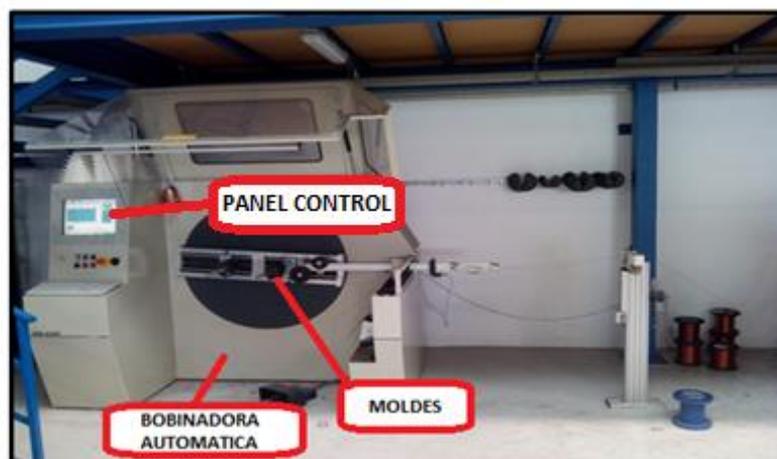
Bobinadora automática. Fuente: Elaboración propia.
